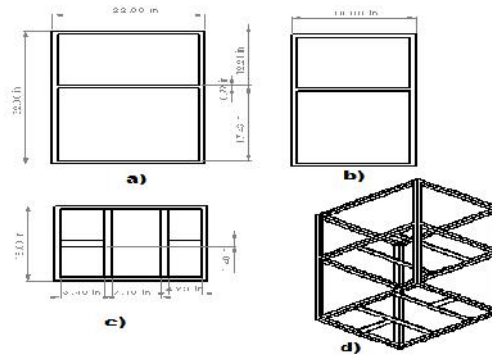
Dimensiones de la estructura, a) Vista lateral, b) Vista frontal, c) Vista superior, d) Vista de estructura completa.
